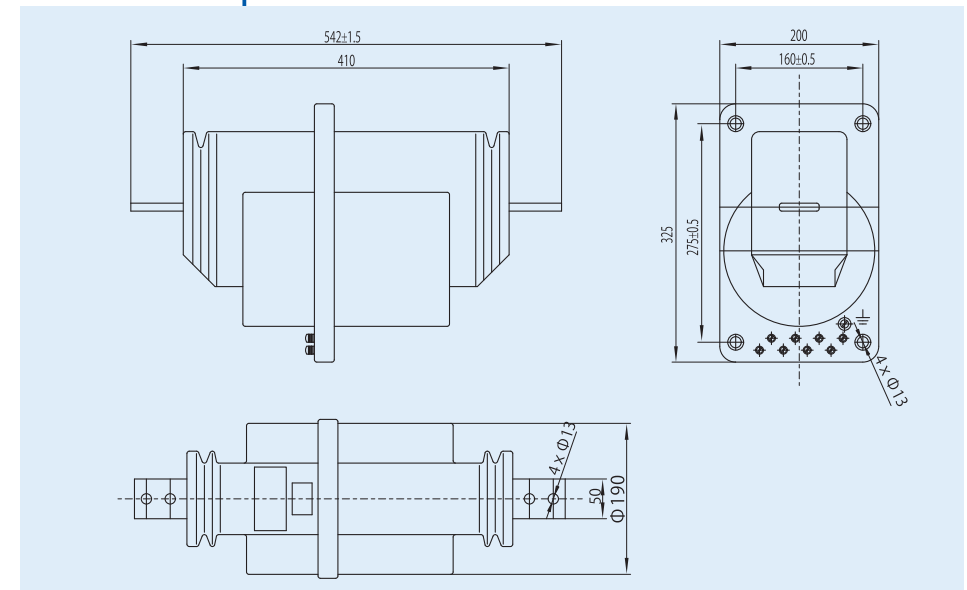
Внешний вид и размеры трансформатора тока LFZBJ8-10Q
